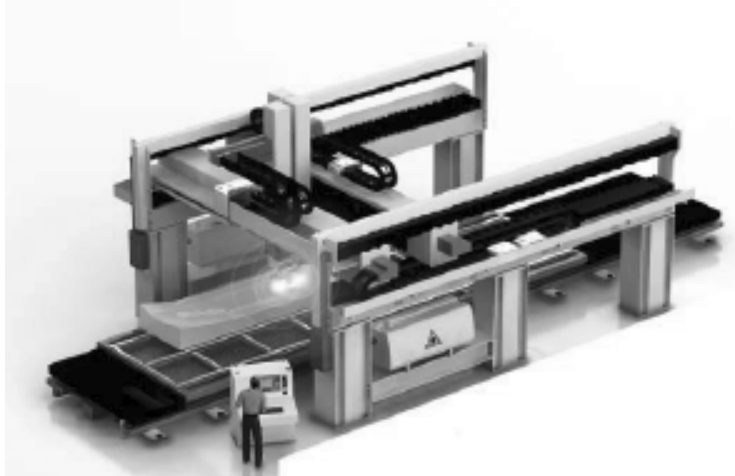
Установка лазерной сварки крупных 3D конструкций
